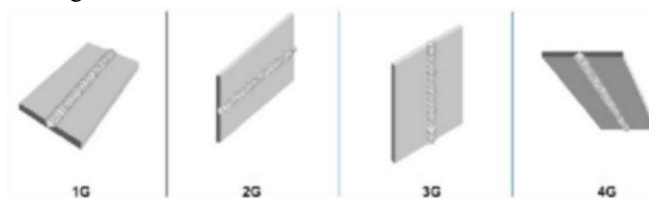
Posiciones de soldadura en ranura (American Welding Society, 2018)
